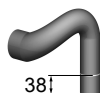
Acortamiento de la manguera, dimensión [mm]
